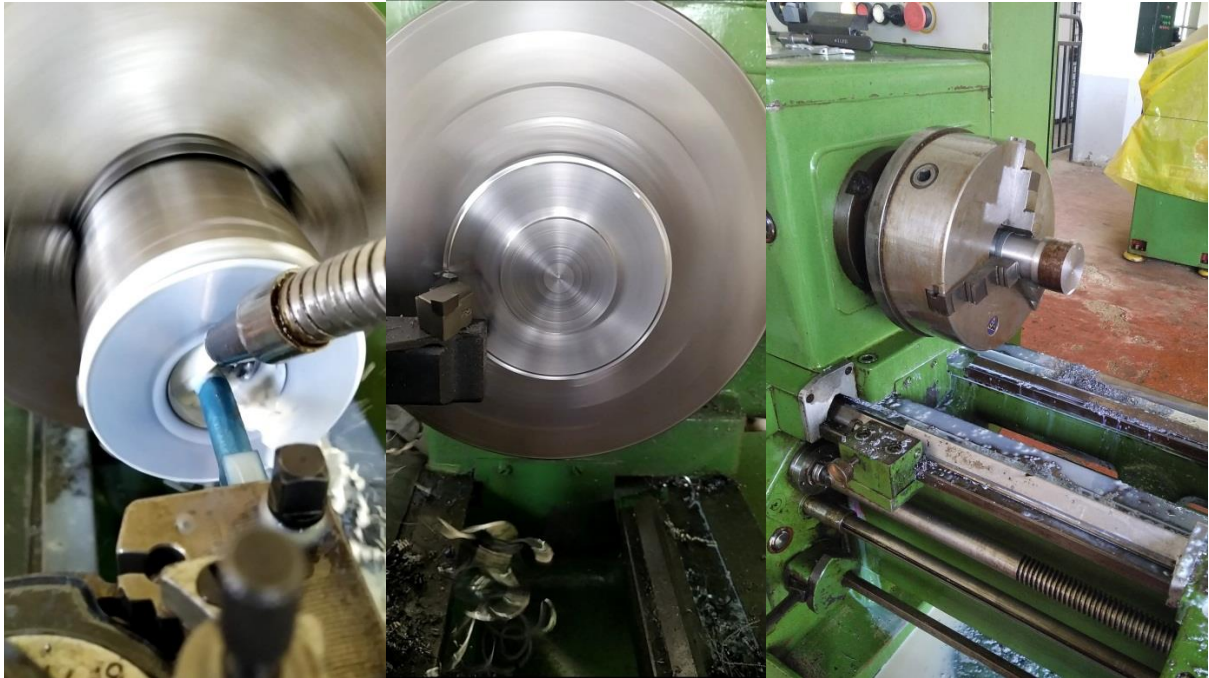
Opération d'usinage du cylindre, du fond et du piston sur tour.
